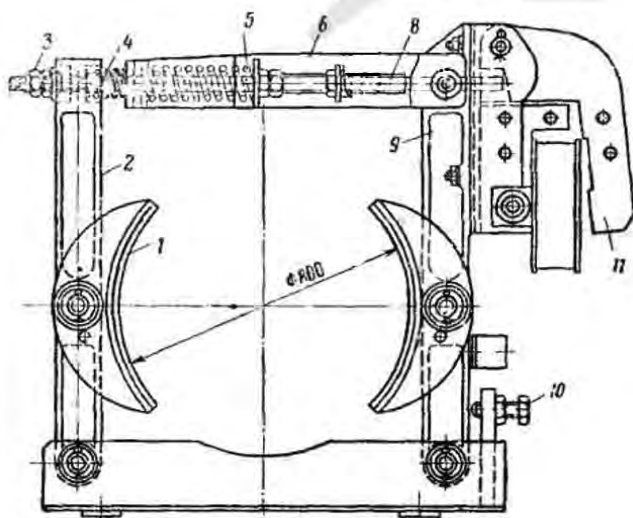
Двухколодочный пружинный электромагнитный тормоз
